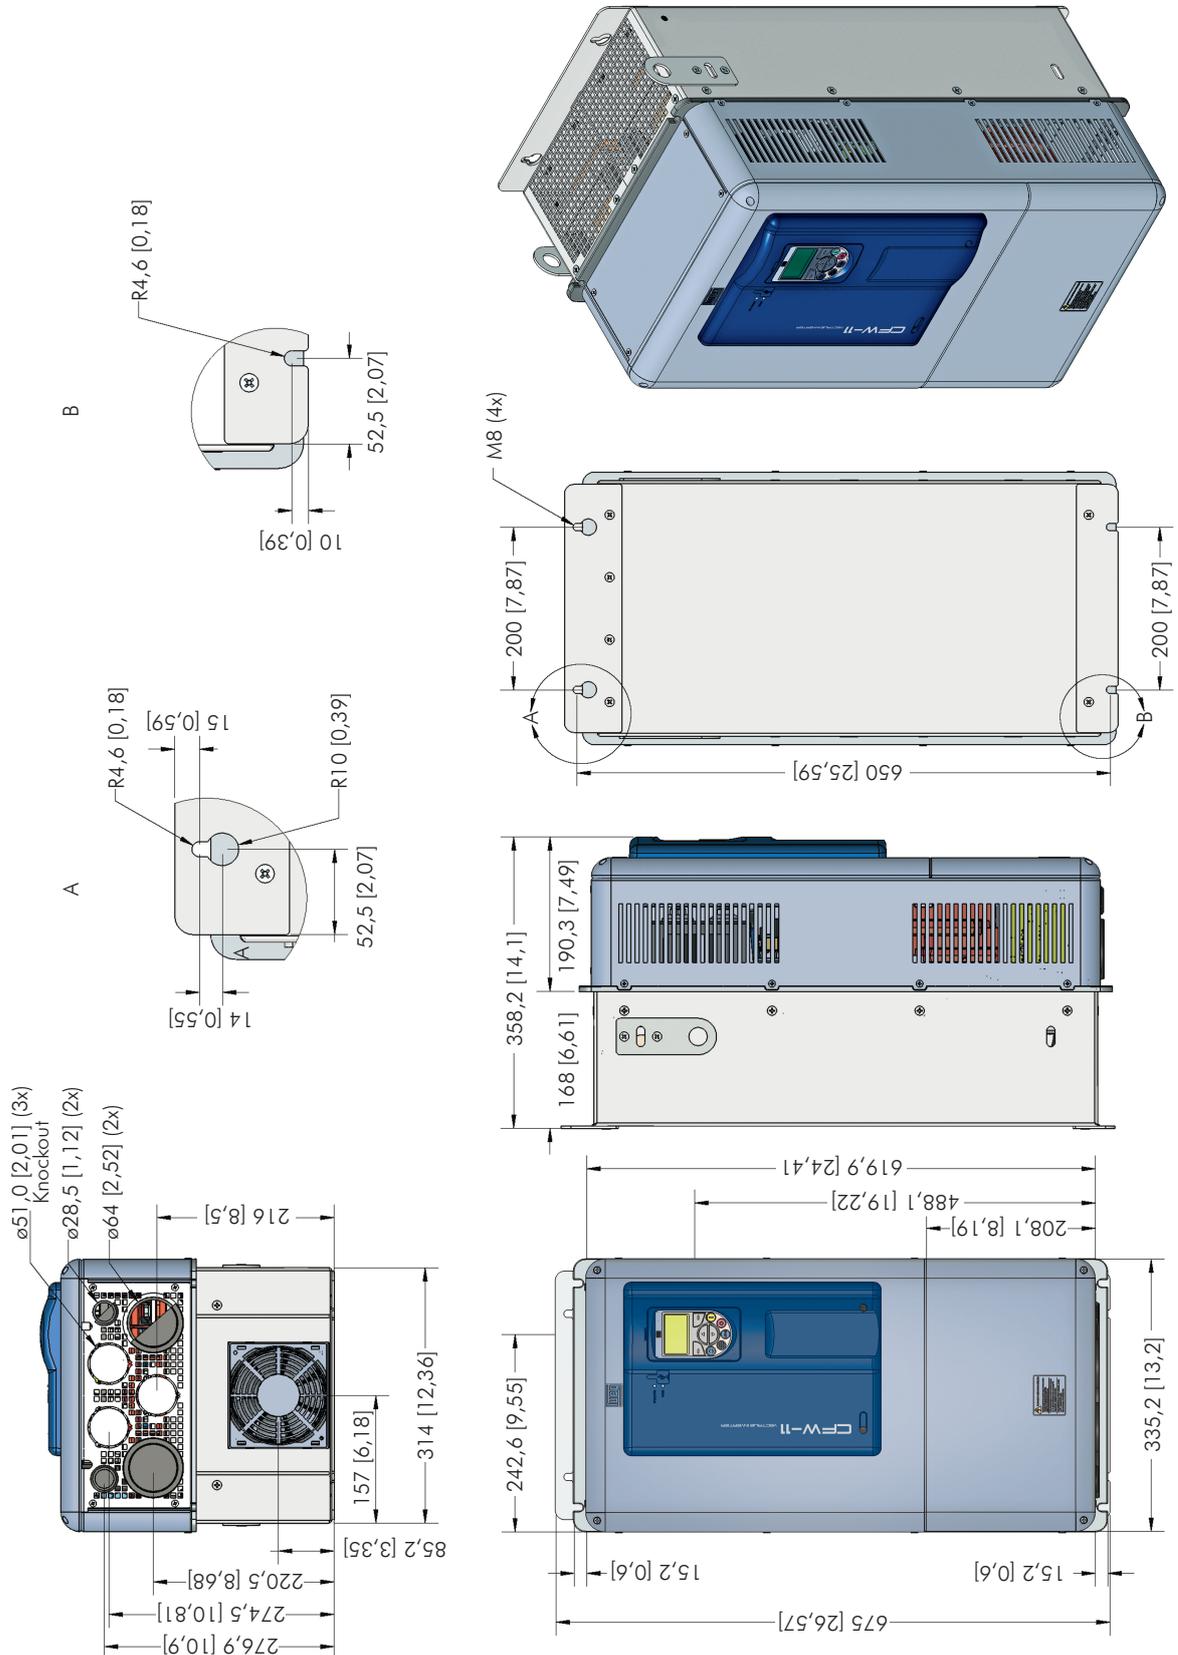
Dimensões do inversor - mecânica E - mm [in]
